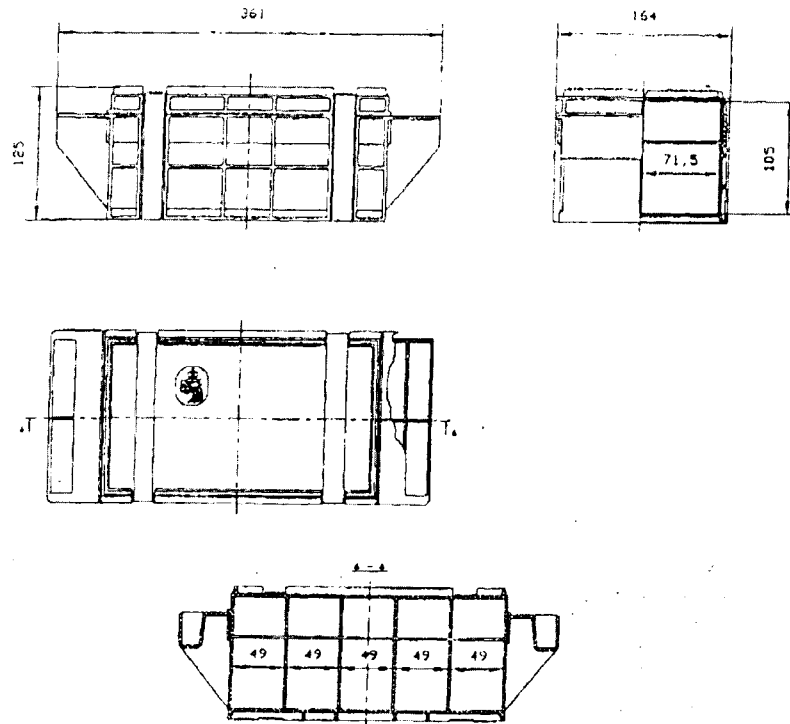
Сборочный чертеж контейнера КТ-10
